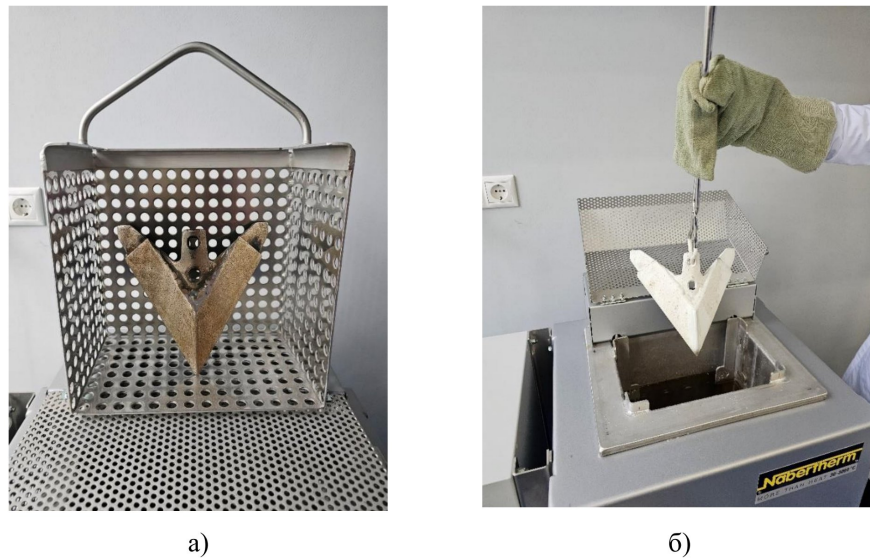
Етапи термічної обробки виготовленої лапи культиватора: а) стан деталі до проведення термообробки; б) вигляд деталі після виконання термообробки.
